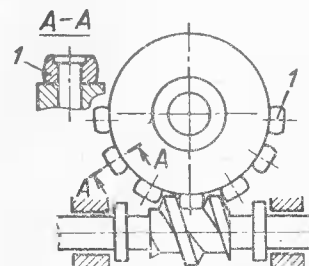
Цилиндрическая червячная передача с зубьями червячного колеса в виде роликов
